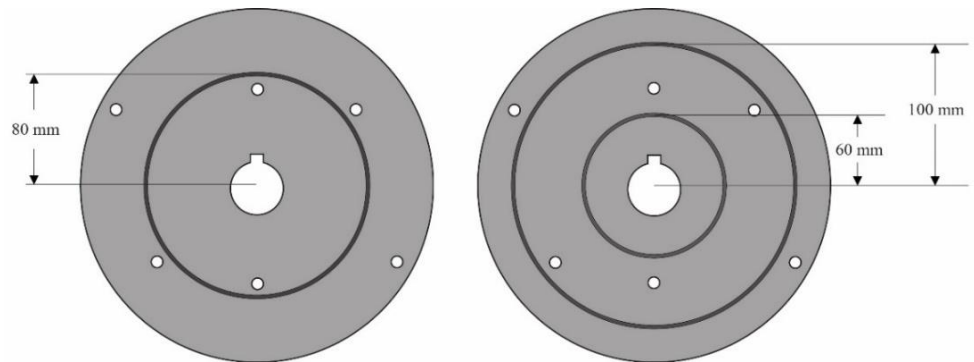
Cara frontal y trasera de la segunda tapa del molde.
